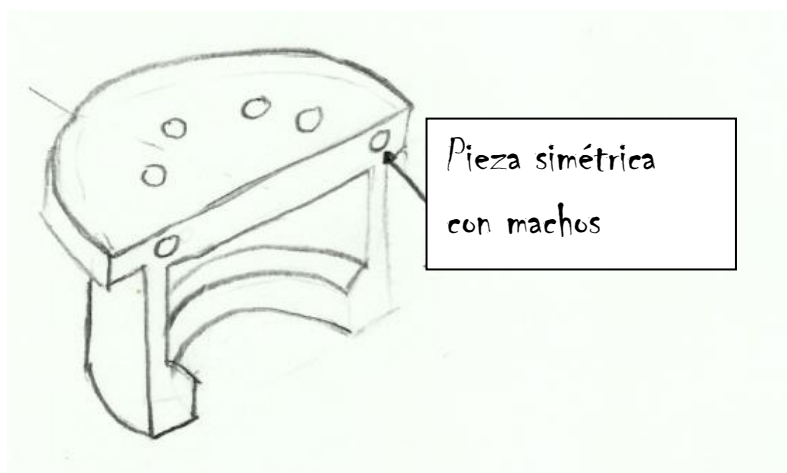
Primer boceto ideado en el diseño de la tapa auxiliar
